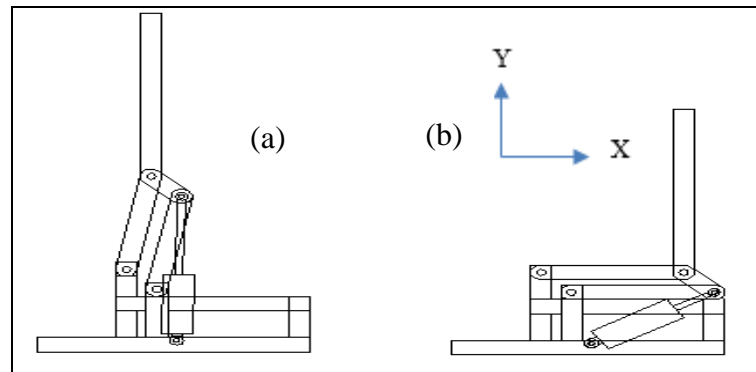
11 Representación plana del mecanismo bipedestador + cilindro actuador. (a) posición final. (b) posición inicial.
